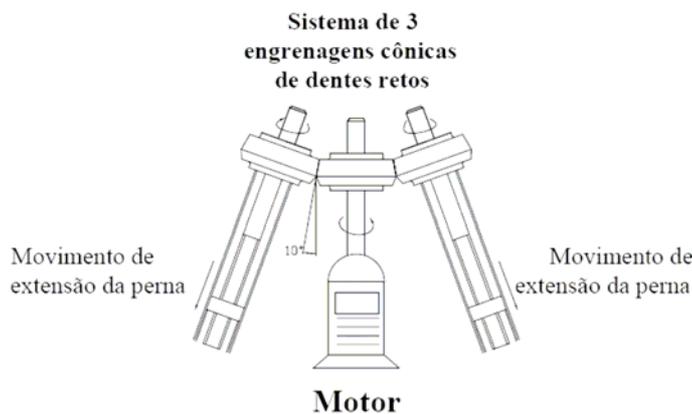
Desenho esquemático do conjunto motor - engrenagens.
